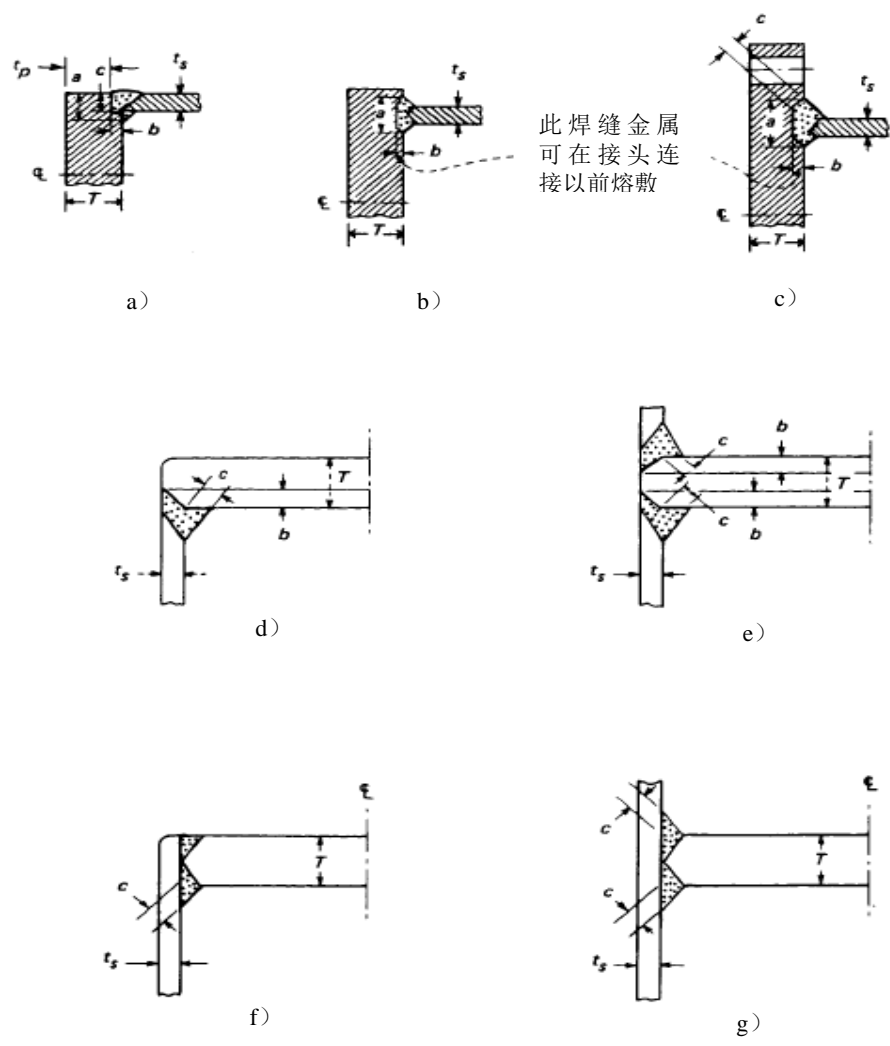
构成角接焊接头的许用全焊透焊缝详图
